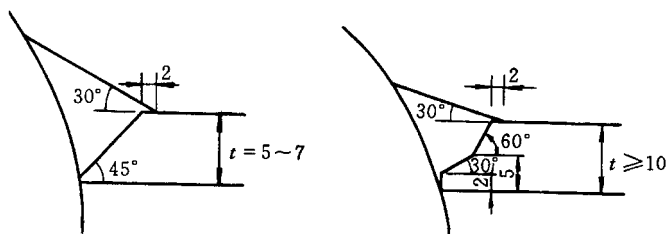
球管焊接接头坡口形式和尺寸
